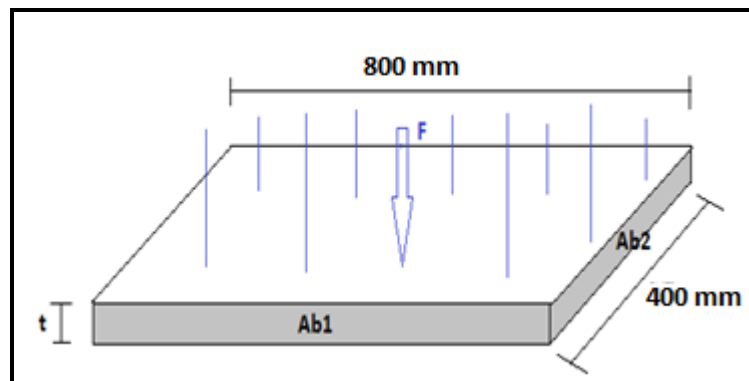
CARGAS SOBRE LA PLACA METÁLICA.
